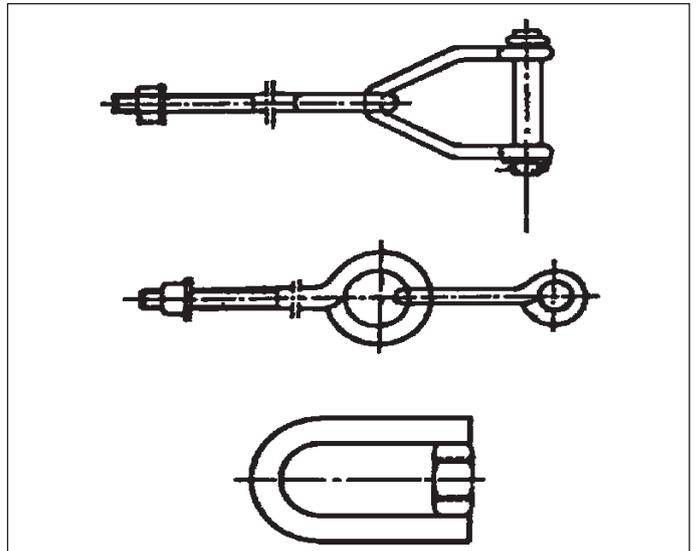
Крепление цепного типа для роликового изолятора и скоба с гайкой.
